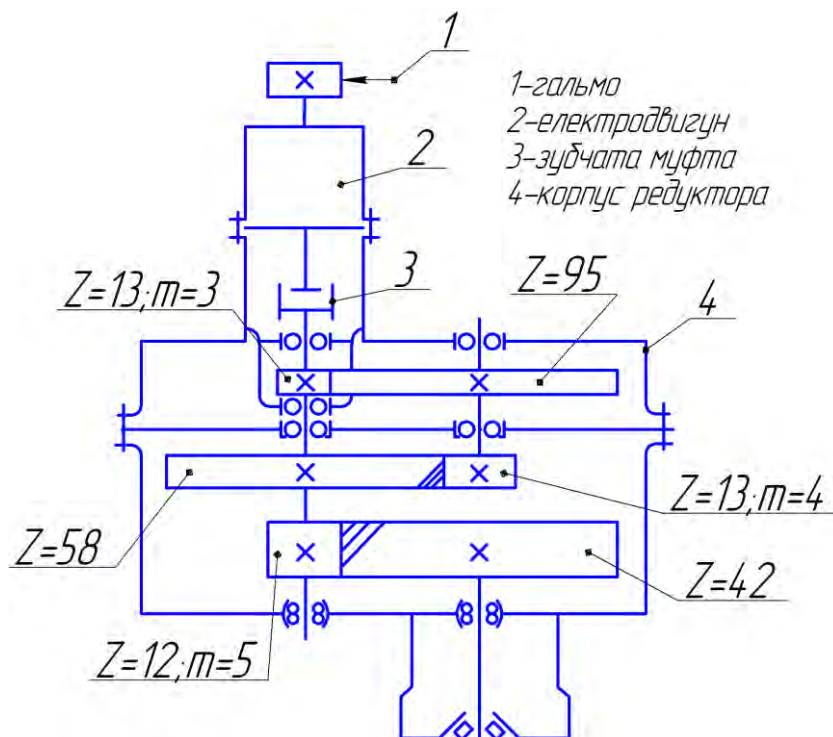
Кінематична схема циліндричного механізму повороту
